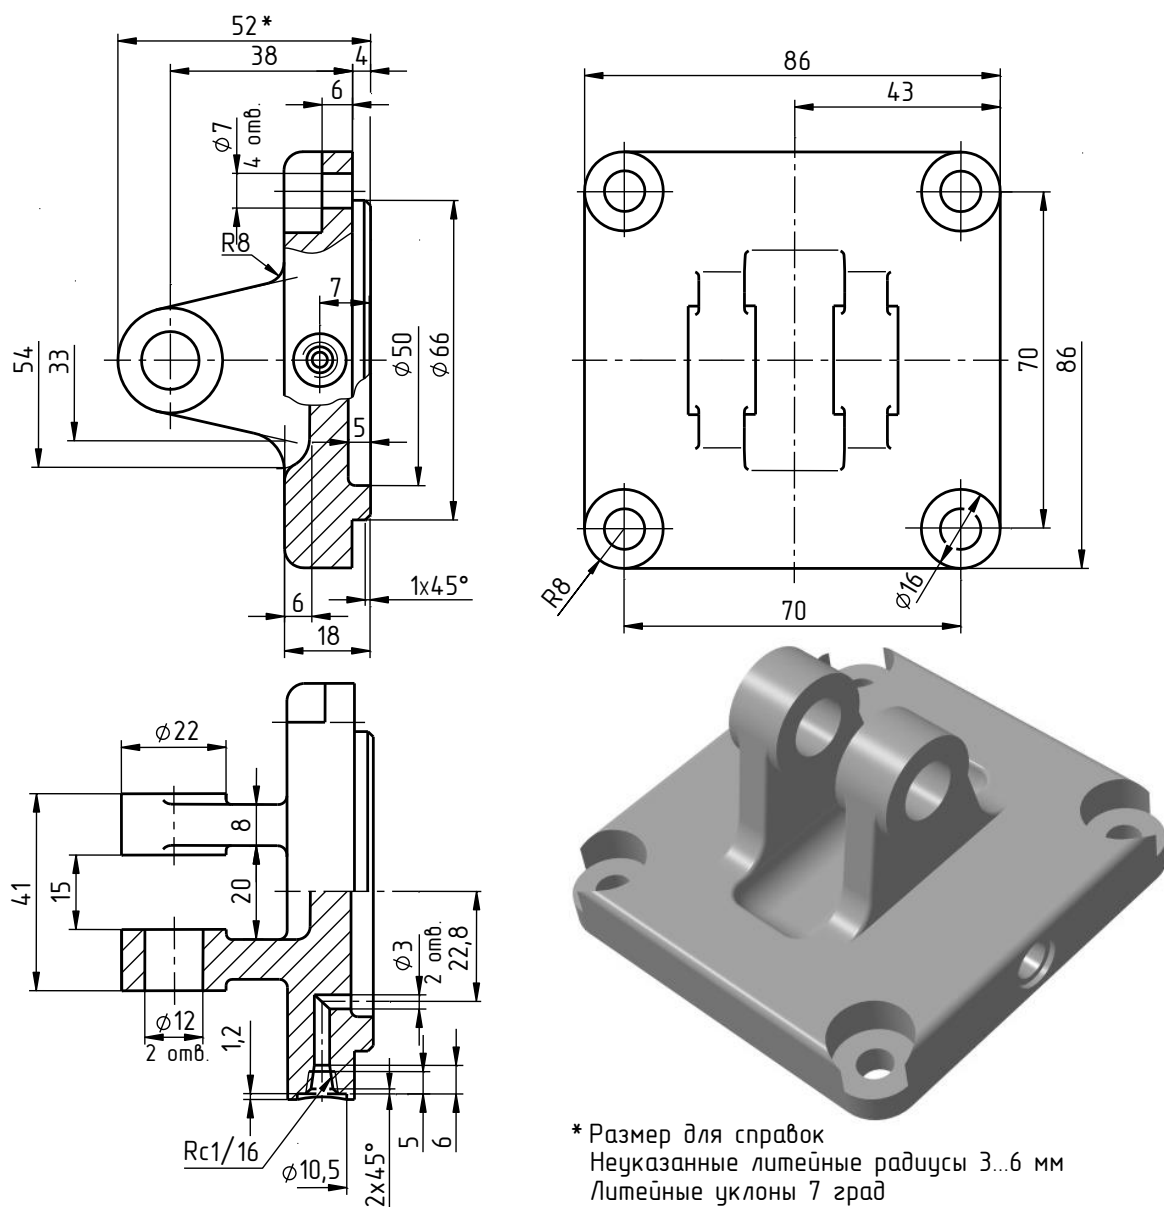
На примере чертежа крышки, заготовка которой была получена методом литья, показано как наносить размеры *скруглений* и координаты вершин скругляемых углов (большинство литейных радиусов указано общей записью)
